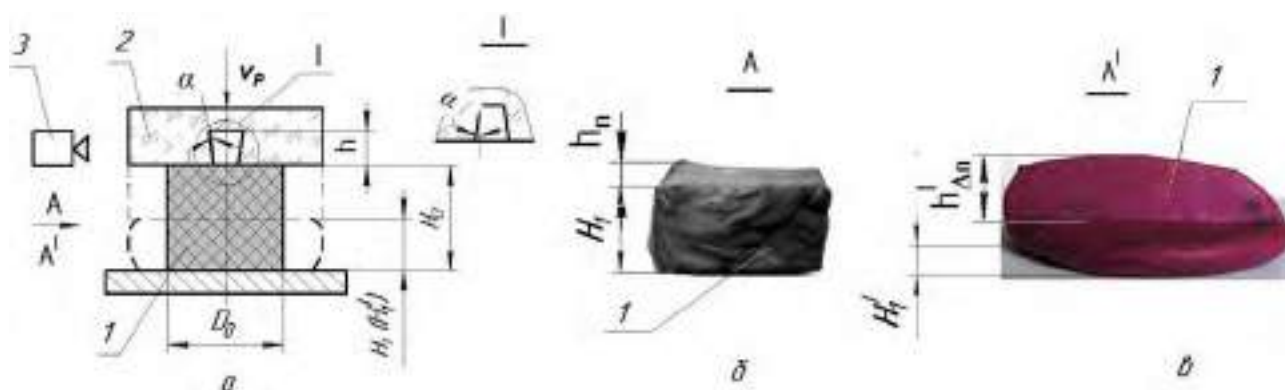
Оптический метод исследования осадки профильной заготовки из пластилина:
